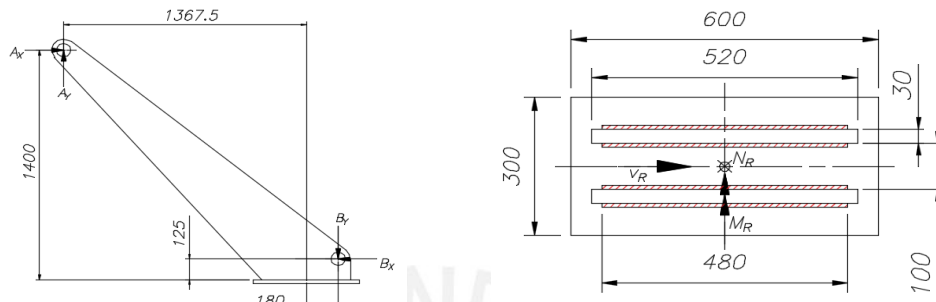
DCL del cordón de soldadura para el soporte de Pluma Telescópica
